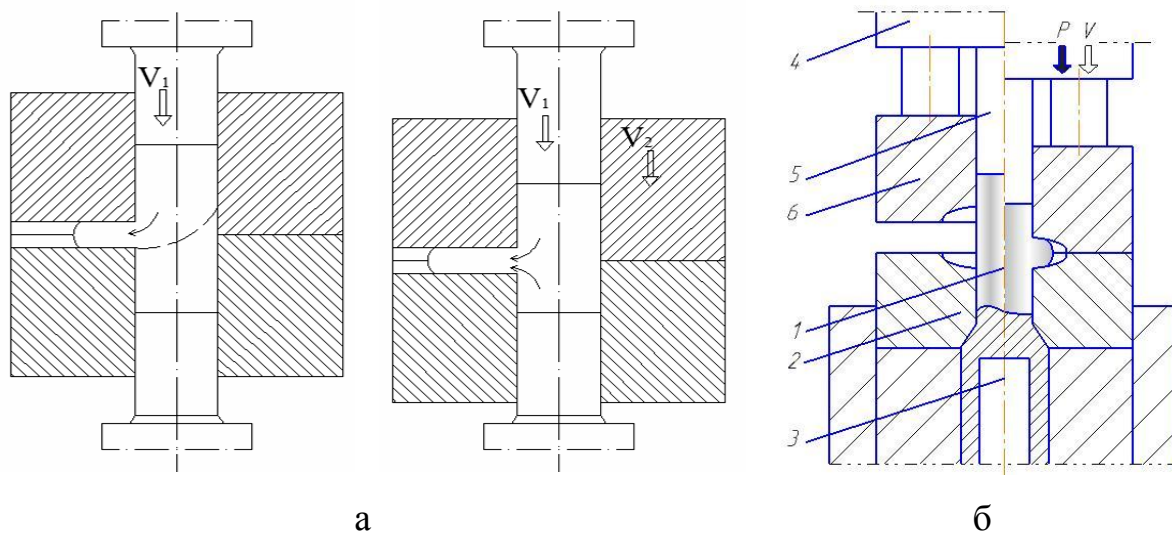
Способи поперечного видавлювання с регульованою подачею металу в порожнину матриці
